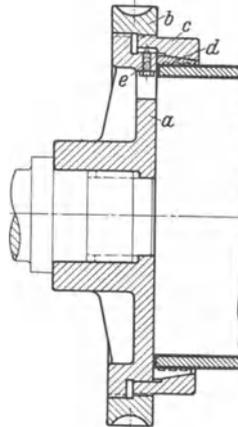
Spannfutter für größere Spanndurchmesser.
